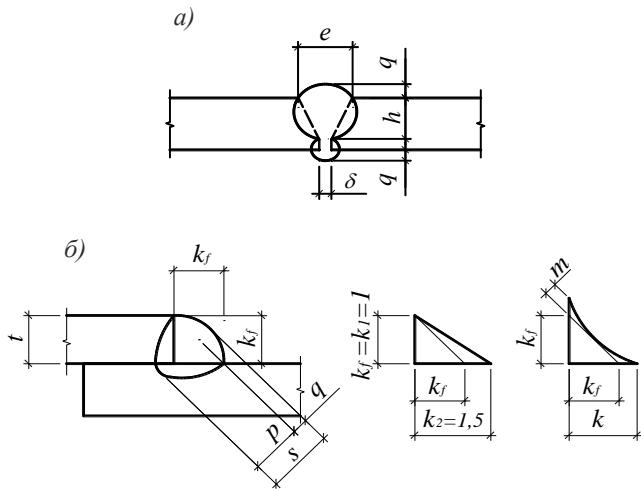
Форма и геометрические размеры сварного шва:
